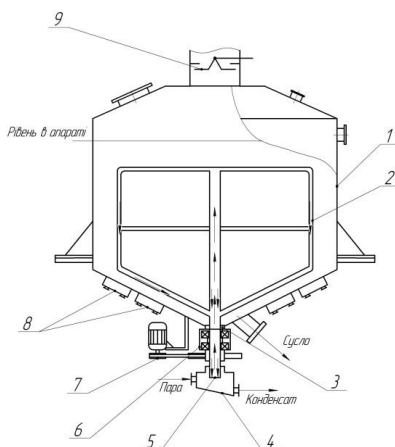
Схема сушловарильного котла з нагрівальним перемішувальним пристроєм: 1 – корпус; 2 – трубчатa мішалка; 3 – ущільнення; 4 – парова камера; 5 – трубовал; 6 – підшипникова коробка; 7 – мотор-редуктор; 8 – парові камери; 9 – конусний шибєр
